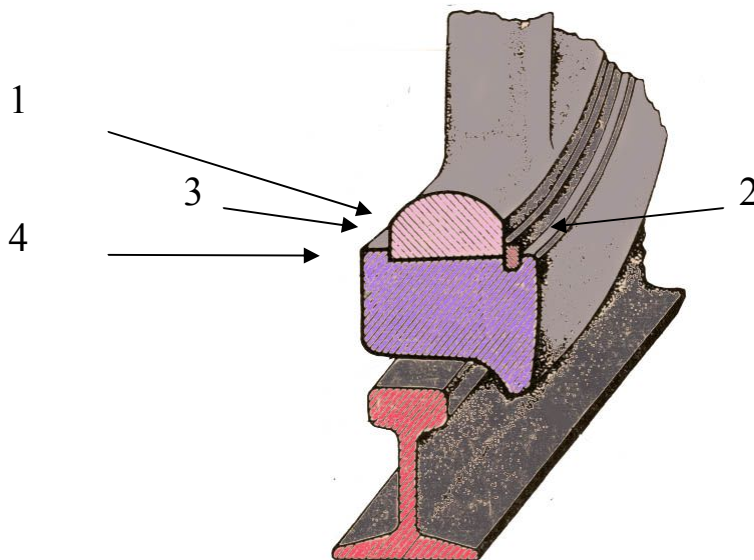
Схема положення колеса на рейці: 1 – бандаж колеса;
